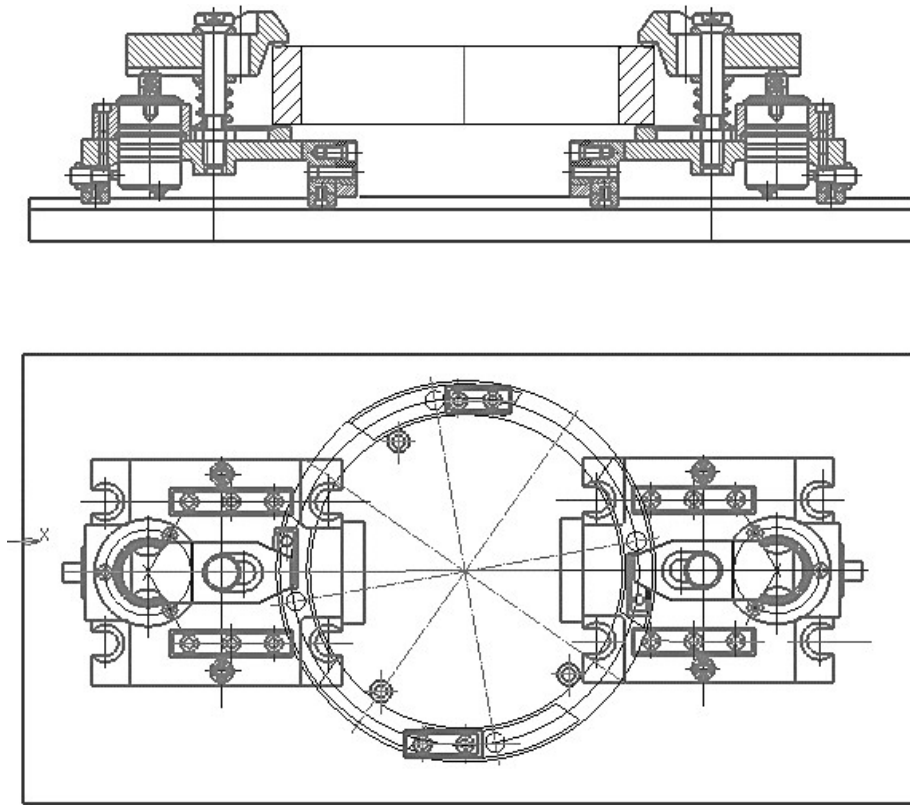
Загальний вигляд пристрою для фрезерування та свердлування
